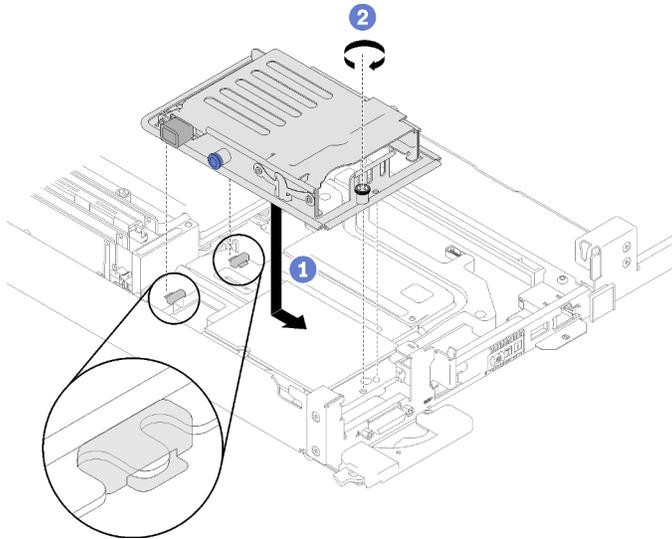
Installation de l'assemblage du boîtier d'unités de disque dur
